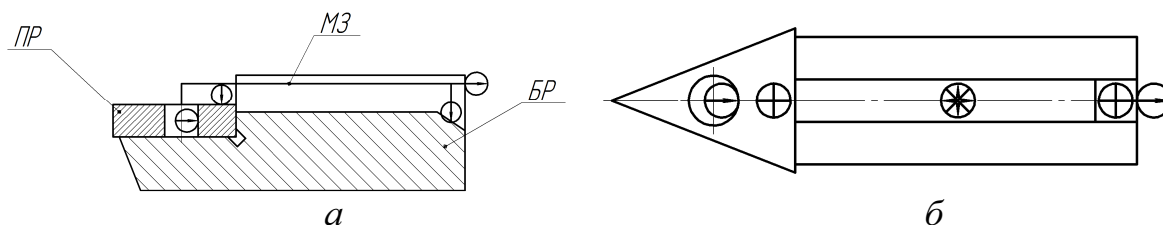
Схема установки пластины режущей в блоке резцовом: *а* – главный вид, *б* – вид сверху; *ПР* – пластина режущая; *БР* – блок резцовый; *МЗ* – модуль зажимной
